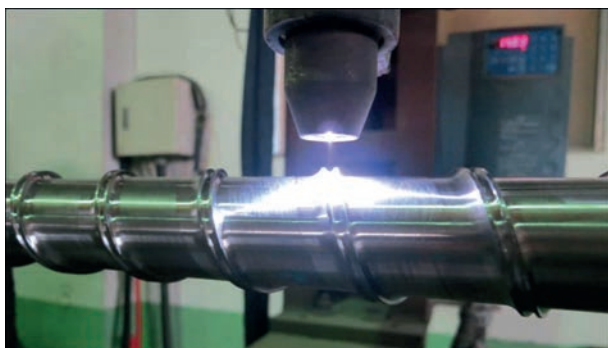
Процес плазмово-дугового наплавлення робочої поверхні шнека [22]
